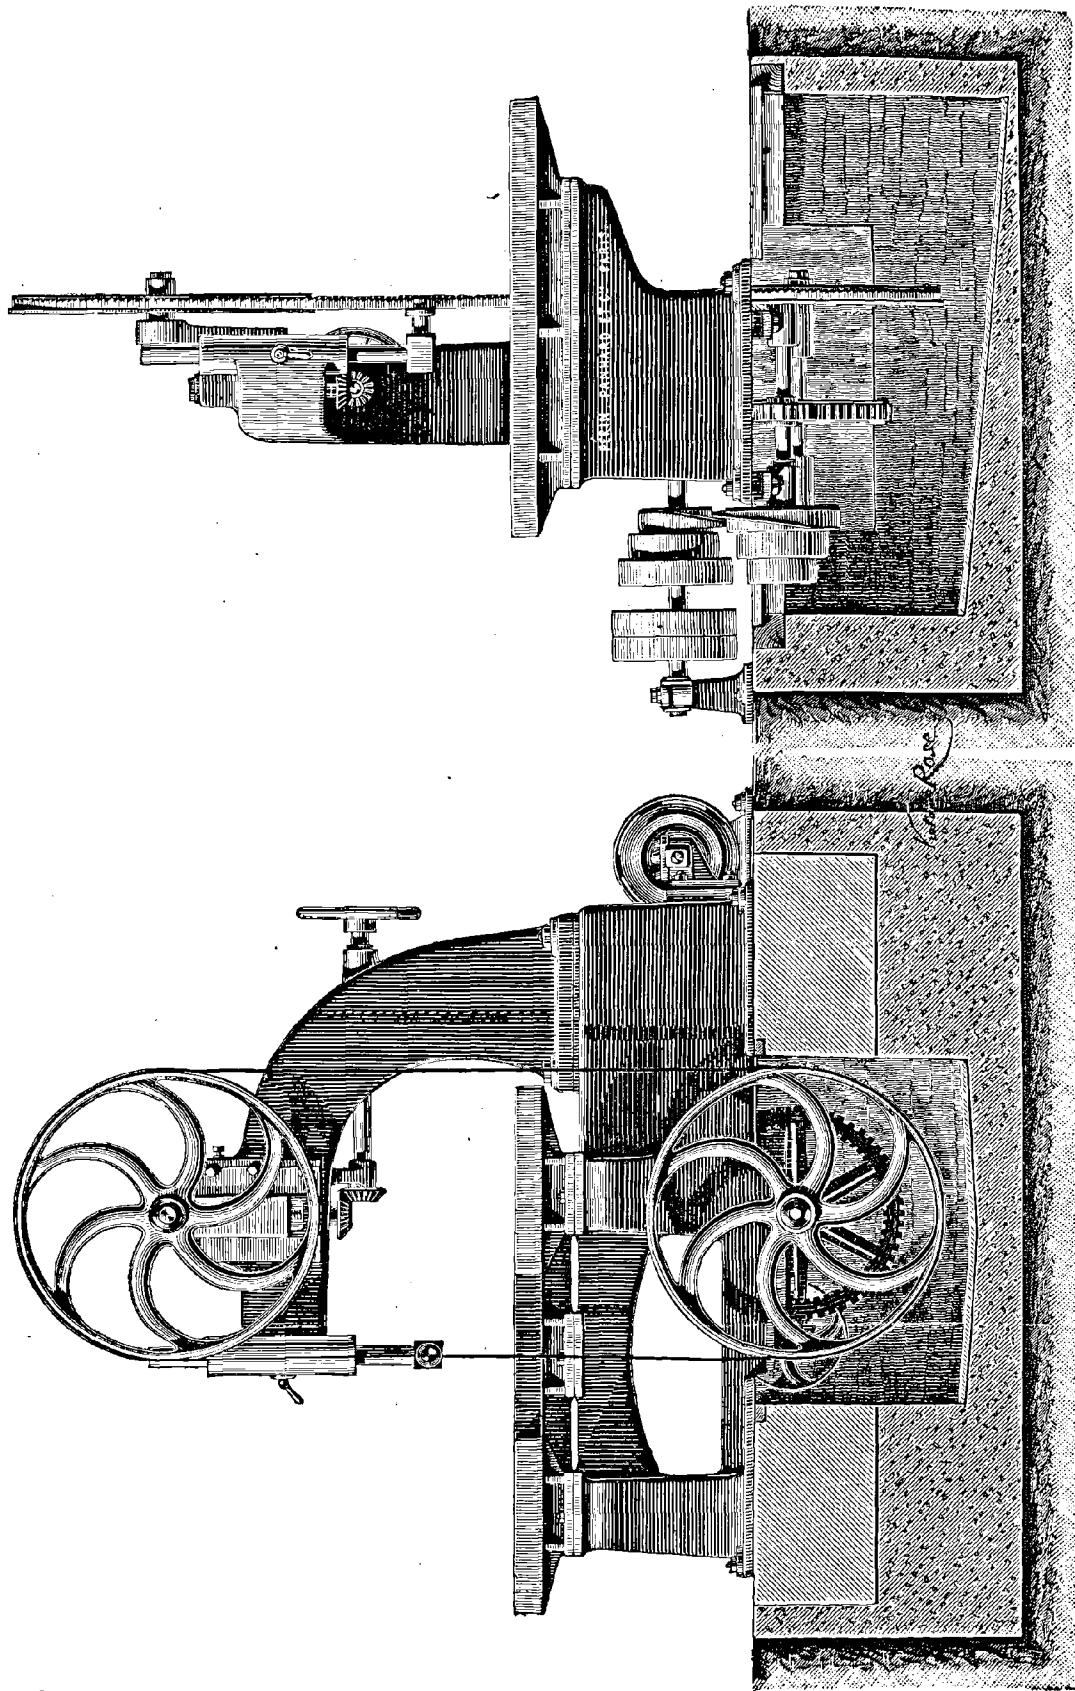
et 820. — Scie à ruban à grande table pour les métaux des Etablissements Panhard et Levassor. — Vue de côté et vue de face.
